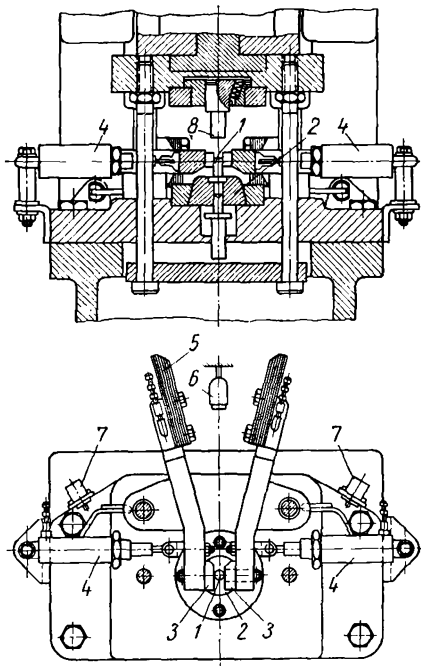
Схема рабочих элементов агрегата для электронагрева и точной высадки болта толкателя
